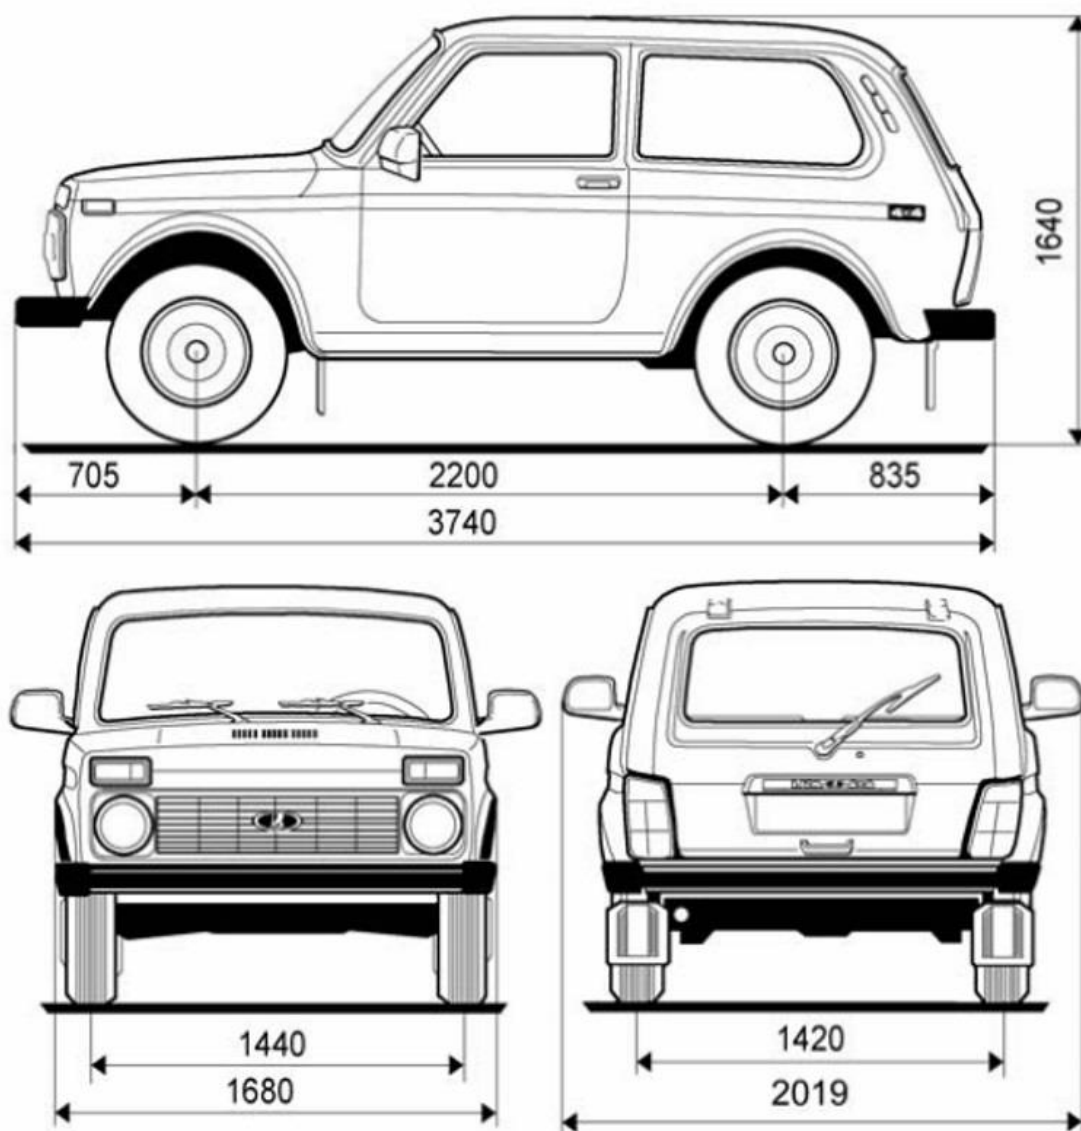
Автомобиль ВАЗ-2121 с указанными внешними габаритными размерами кузова, параметрами колеи и колесной базы
